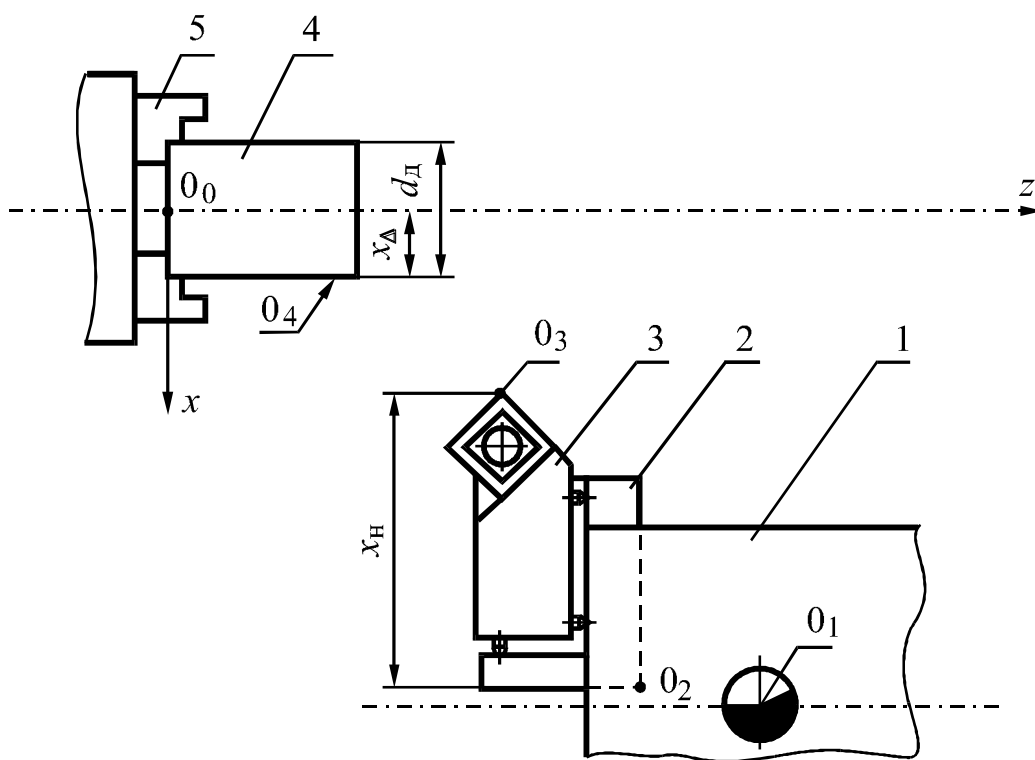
Схема расположения инструмента относительно оси вращения заготовки: 1 – револьверная головка; 2 – держатель инструментального блока; 3 – резец; 4 – заготовка; 5 – патрон (0_0 – начало координат станка; 0_1 – точка, расположенная на оси вращения головки; 0_2 – точка на базовой поверхности гнезда револьверной головки; 0_3 – вершина резца; 0_4 – точка на поверхности заготовки)
